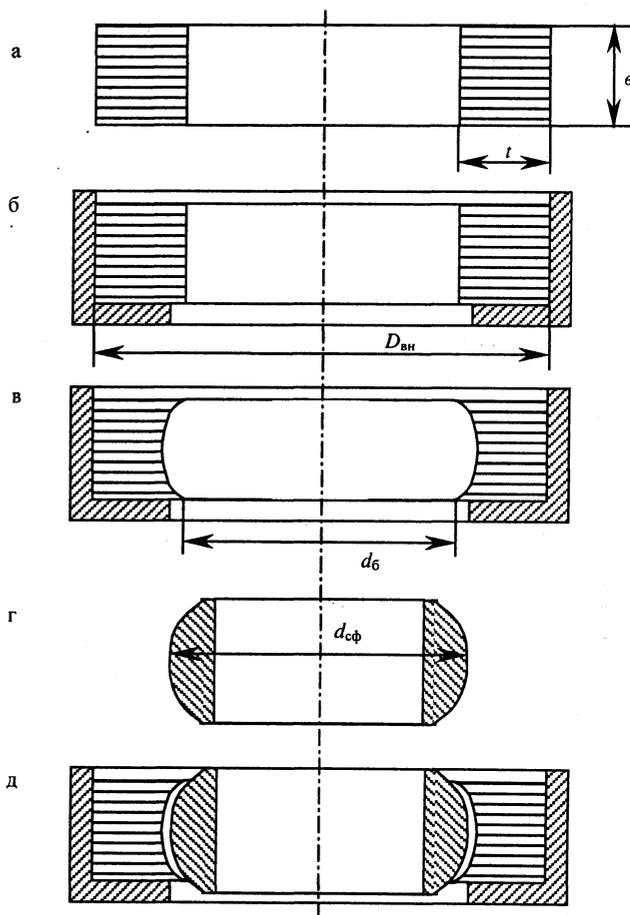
Самоустанавливающийся подшипник скольжения: а – втулка торцово-прессового деформирования; б – подшипник скольжения самосмазывающийся; в – подшипник с внутренней сферической поверхностью; г – внутреннее металлическое кольцо со сферической наружной поверхностью; д – готовый подшипник
